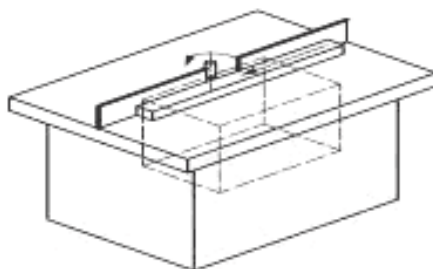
Одношпиндельный вертикальный строгально-калевочный станок
